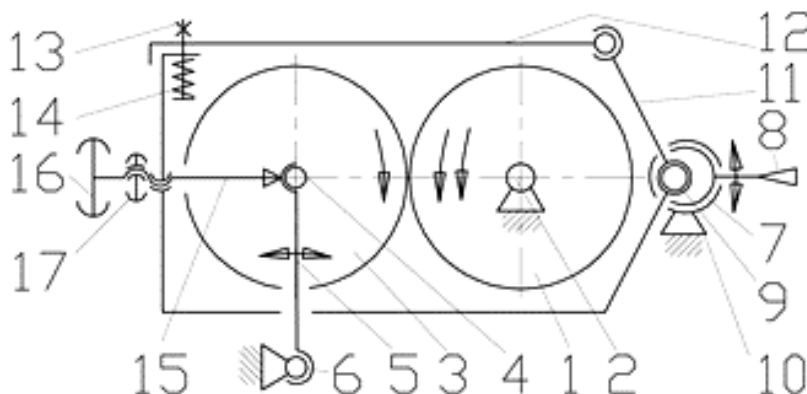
Схема установчого механізму вальцьового верстата.
